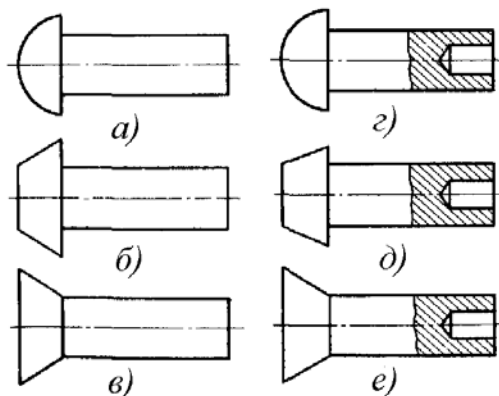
Стандартные стальные заклепки с различной формой головок
